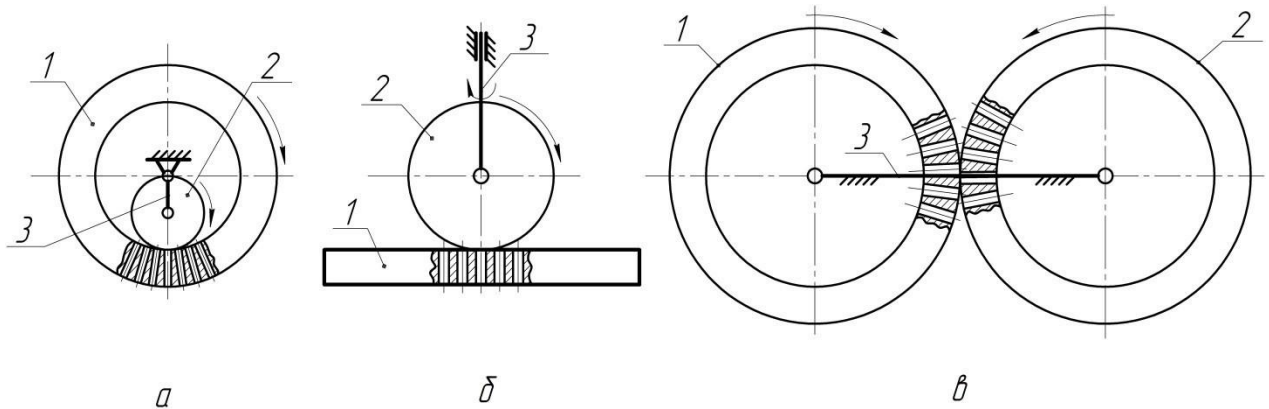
Схеми механізмів пресування з циліндричними робочими органами [33]: *a* – робочі механізми з внутрішнім контактом; *б* – з плоскою матрицею; *в* – робочі механізми із зовнішнім контактом
